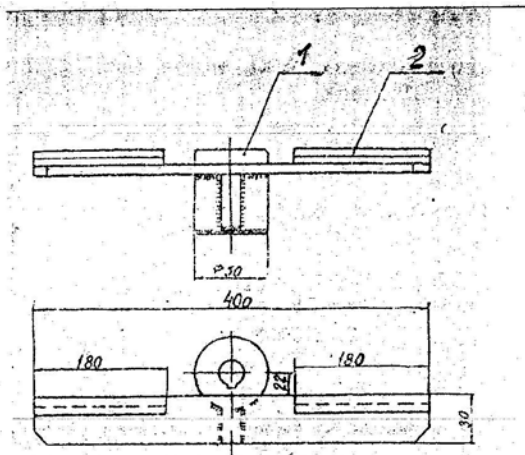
Приспособление для обрезки и насечки зубьев рамных пил
